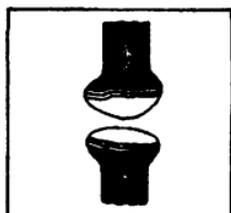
Подготовка концов под горновую сварку
